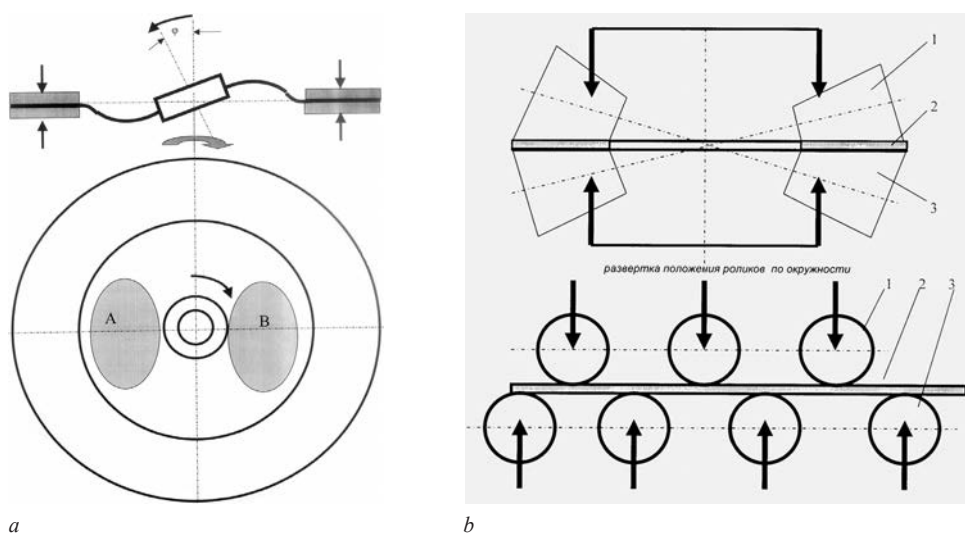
Конструктивная схема устройства для стабилизации кольцевых заготовок типа диск:
